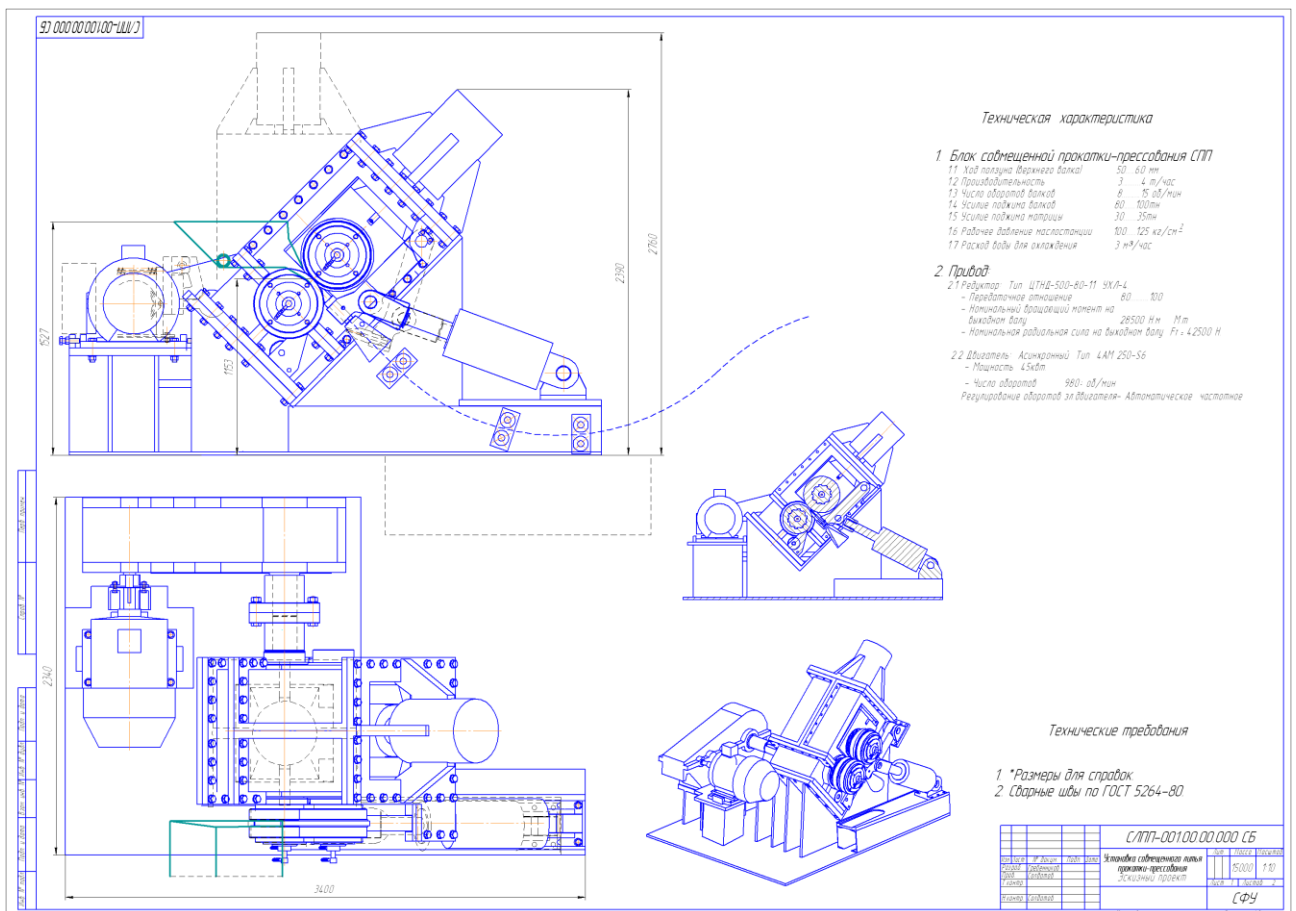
Рабочий чертеж установки СЛИПП-2,5
